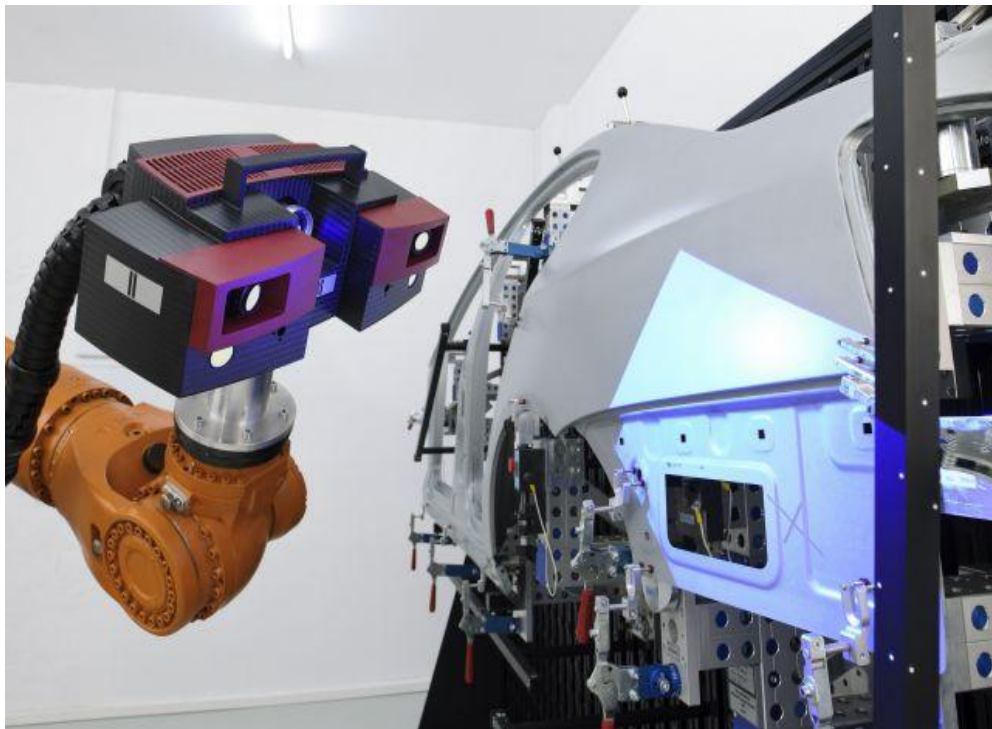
Sloupový dvouramenný měřicí 3D skener Dimension [7].
